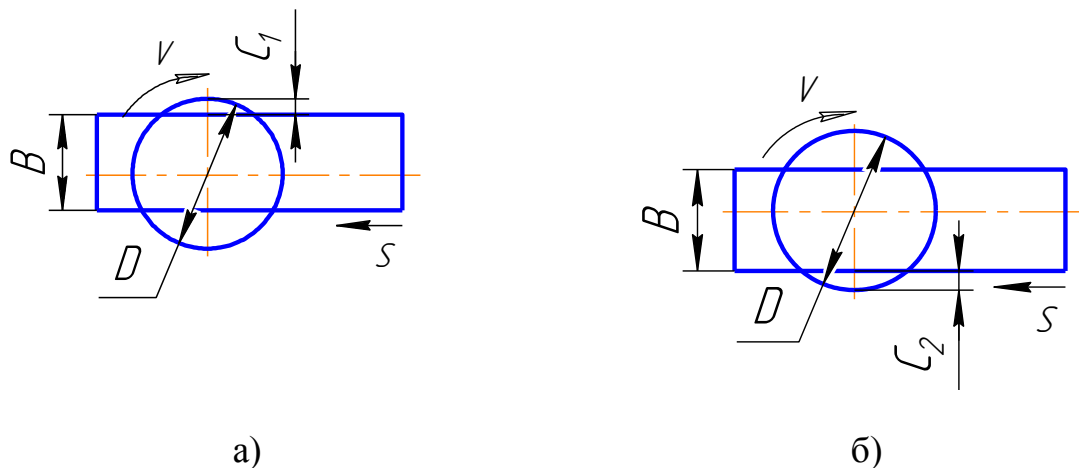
Розташування сталеві заготовки при торцевому фрезеруванні щодо фрези: а – врізання зуба фрези при $c_1 = (0,03 \div 0,05) \cdot D$; б – вихід зуба фрези при $c_2 = 0$.
